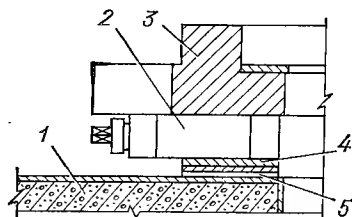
Установка опоры корпуса клиновыми домкратами.
